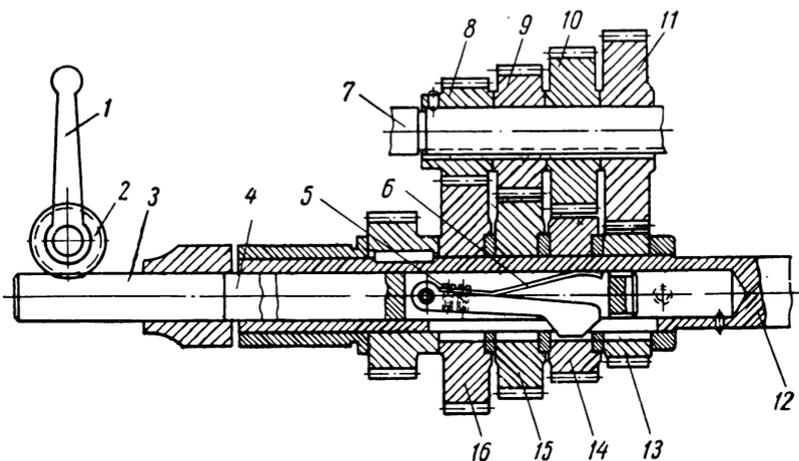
Схема устройства коробки подач с вытяжной шпонкой
